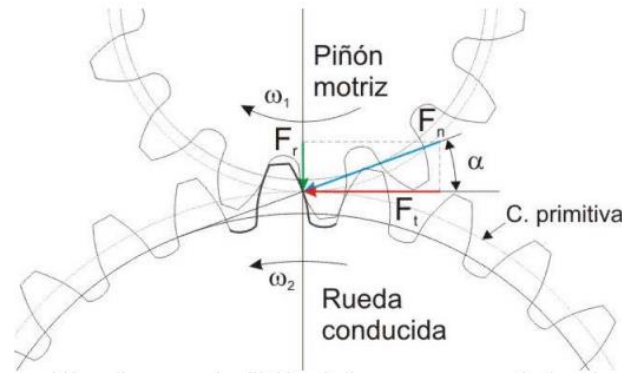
TRANSMISIÓN MEDIANTE ENGRANAJES CILÍNDRICOS DE DIENTES RECTOS. FUERZAS SOBRE LA RUEDA CONDUCTADA
